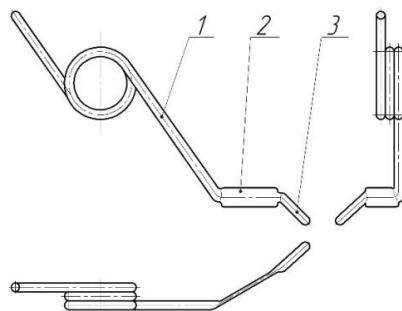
Конструктивна схема загортача просапної сівалки: 1 – стрижень пружини; 2 – пластина; 3 – зрушувач.
